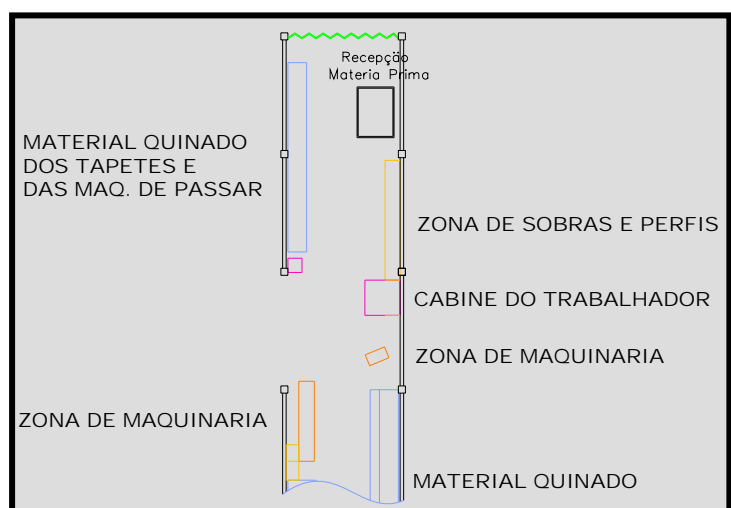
Planta da zona de Sobras e Equipamentos de Trabalho
